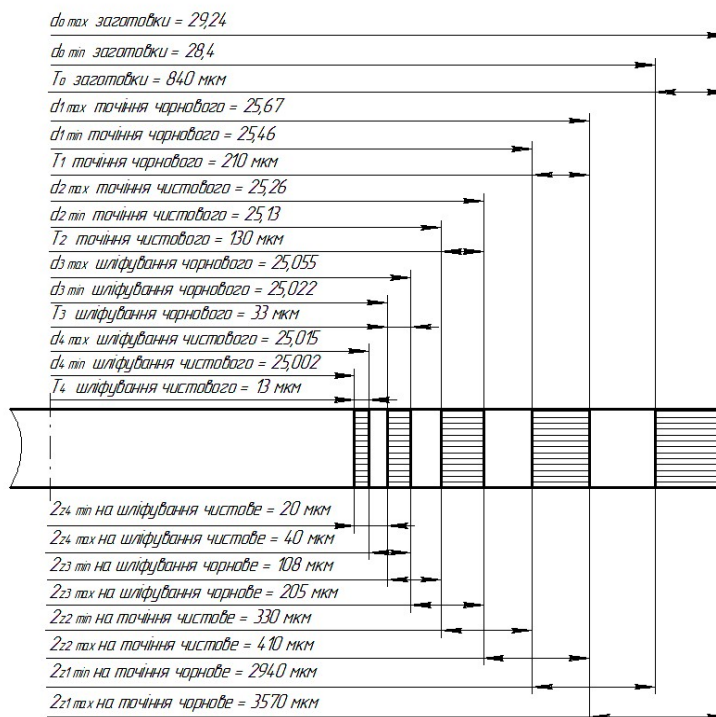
Схема розташування полів припусків і допусків на обробку поверхні $\varnothing 25$ k6 ($+0.015$ / -0.002).
